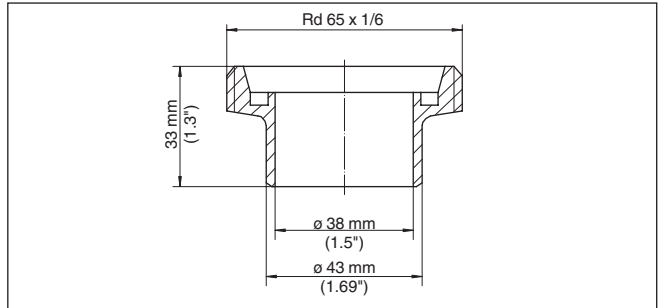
Maße Einschweißstutzen Rohrverschraubung DN 40 (DIN 11851)
